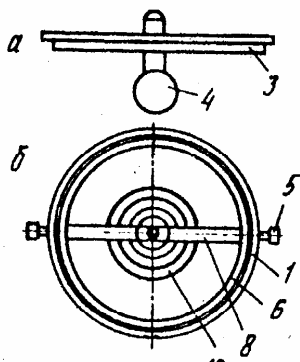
Вид сверху механизма без крышки (б) и вид крышки сбоку (а)
